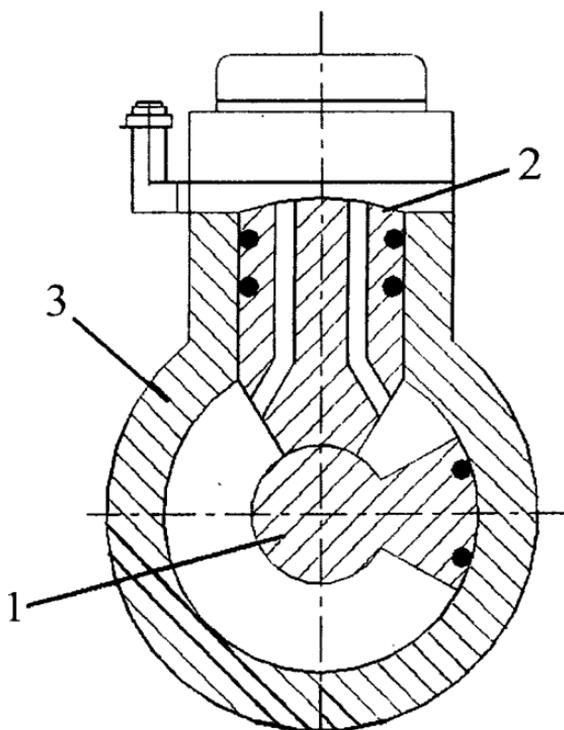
Схема неполноповоротного гидродвигателя:
